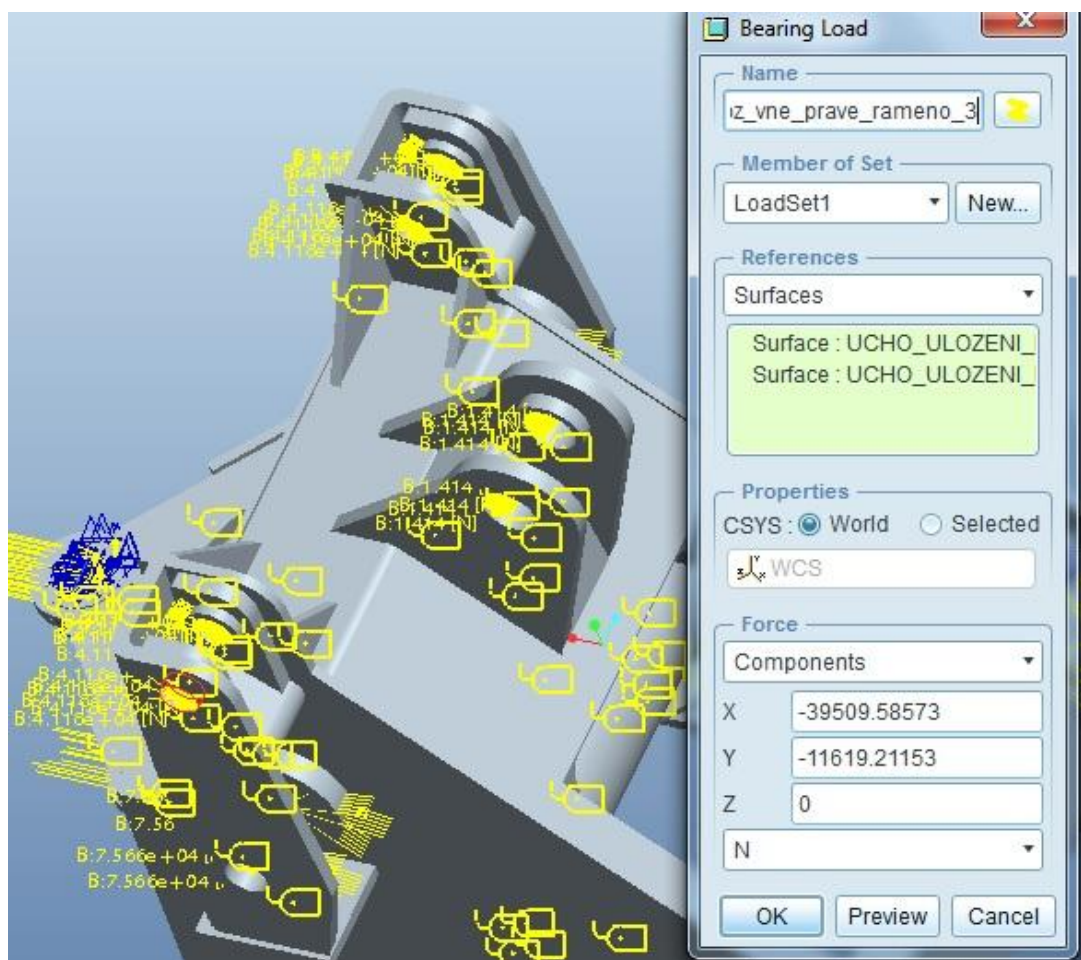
silové působení zadního rámu na přední v místě čepového spojení
